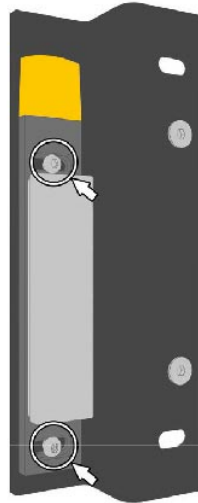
Ankerplatte an Montageplatte anbringen und Schrauben M6 x 8 mm Torx festziehen.
